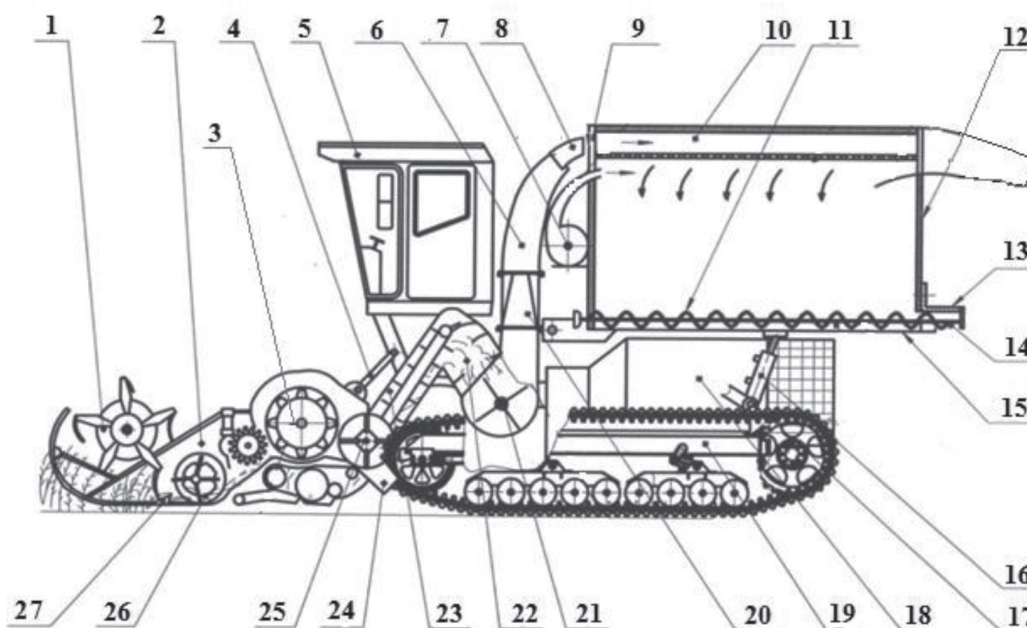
Полевая машина для сбора зерносоевого вороха: 1 – мотовило; 2 – корпус жатки; 3 – роторное молотильно-сепарирующее устройство (МСУ) с тангенциальной подачей хлебной массы; 4 – передняя навеска; 5 – кабина с органами управления; 6 – поворотная часть; 7 – вентилятор; 8 – козырек; 9 – передняя стенка бункера; 10 – бункер-накопитель; 11 – два шнека одного направления навивки; 12 – задняя стенка бункера; 13 – кожух; 14 – выгрузное устройство; 15 – днище бункера-накопителя; 16 – гидроцилиндры; 17 – рама энергосредства; 18 – моторная установка; 19 – гусеничный движитель; 20 – конфузор; 21 – ускоритель движения зернового вороха в виде лопастного вентилятора; 22 – гибкий гофрированный патрубок; 23 – элеватор; 24 – соломоотвод; 25 – измельчитель; 26 – шнек; 27 – режущий аппарат
